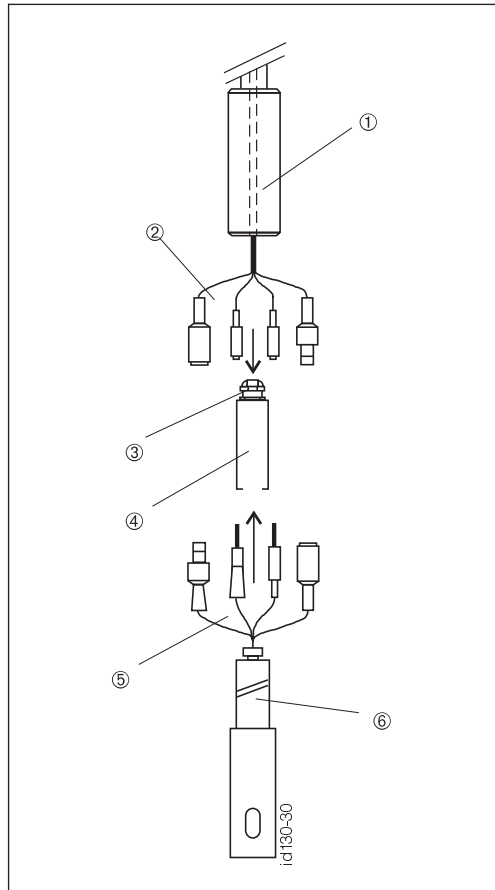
Raccordement par câble et montage du capteur à immersion
